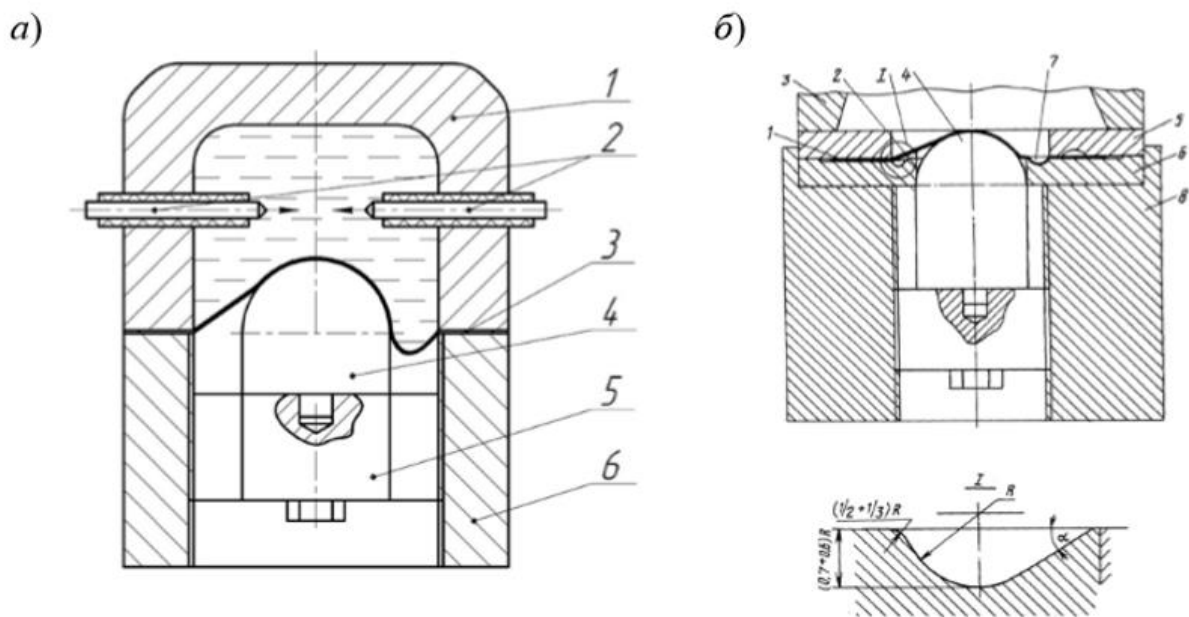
Технологічні схеми інтенсифікованої ЕГІ витяжки-формування К.І. Поздова: а – глибока статико-імпульсна витяжка [101]; б – статико-імпульсна витяжка з резервуванням матеріалу в кільцевих канавках на фланці: 1 – листова заготовка; 2 – вставка; 3 – розрядна камера; 4 – пуансон; 5 – верхній диск; 6 – нижній диск; 7 – виїмка; 8 – корпус
